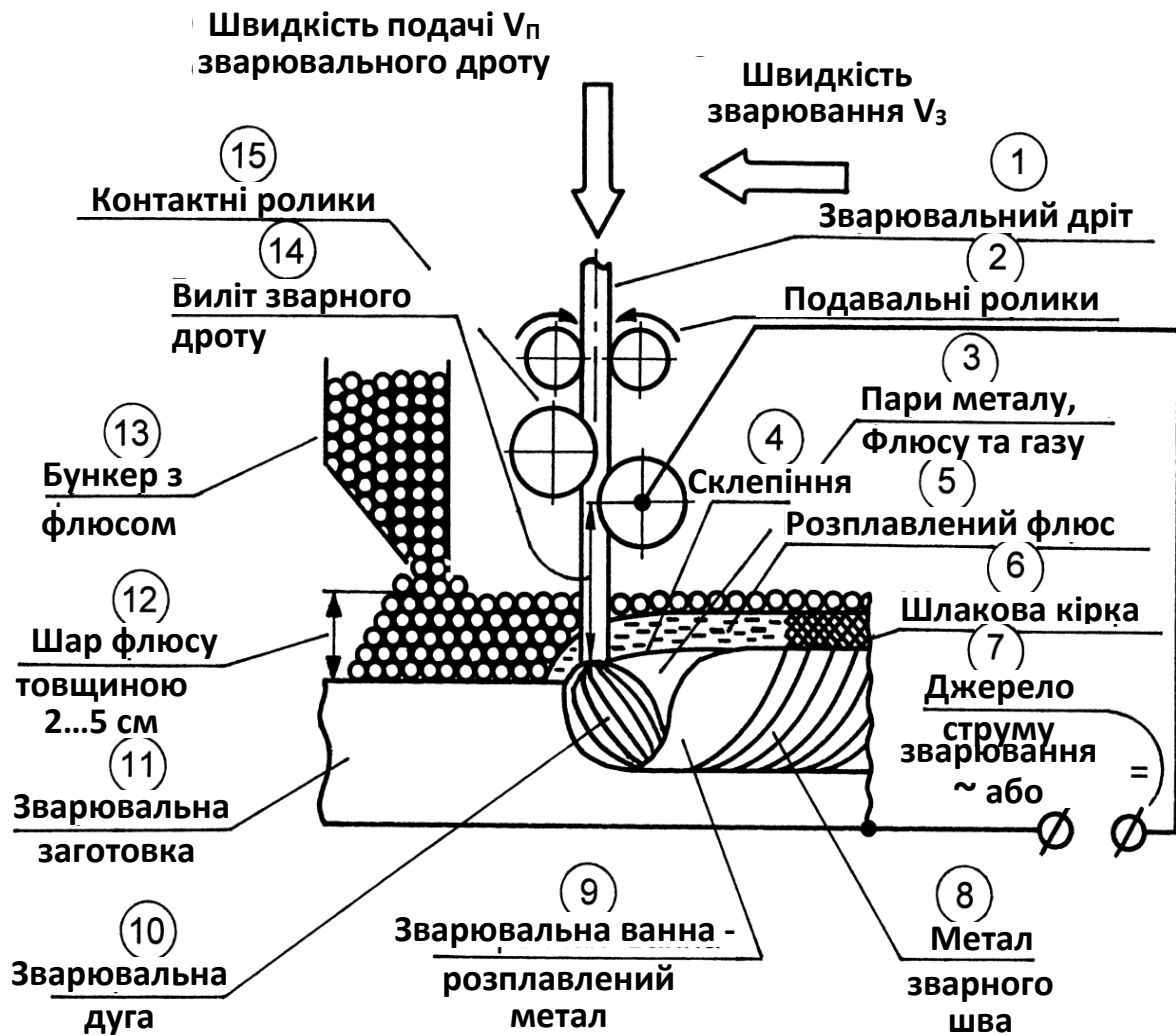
Схема процесу автоматичного зварювання під шаром флюсу
